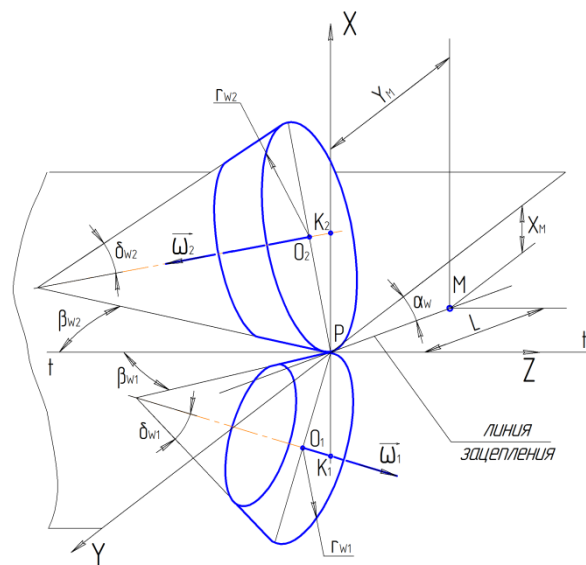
Начальные поверхности гиперболоидной зубчатой передачи
